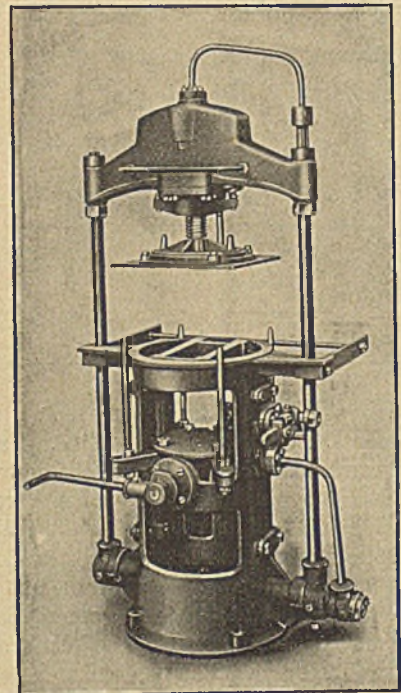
Druckwasserformmaschine mit zurückschwenkbarem Preßholm.
